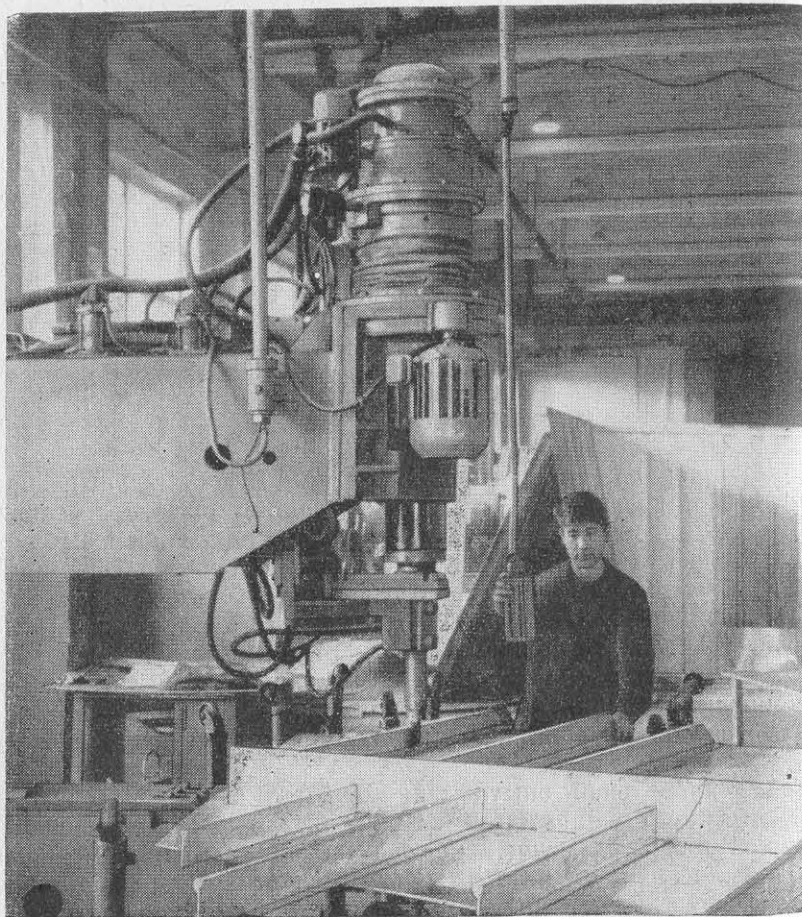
Контактная приварка набора при комбинированном способе сварки.
